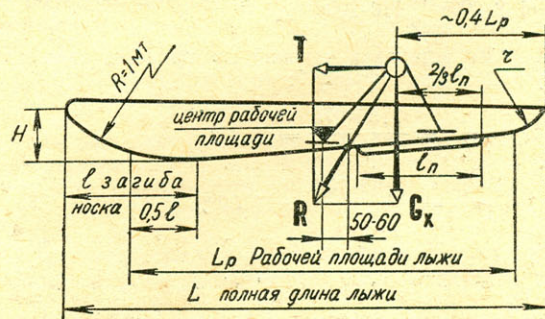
Схема увязки размеров лыжи аэросаней (L_p — длина несущей поверхности лыжи).
